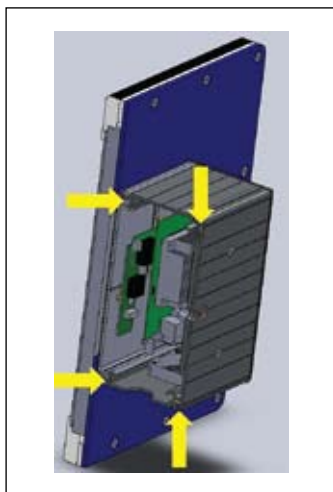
Конструкция замка корпуса блока управления (поперечный разрез)
